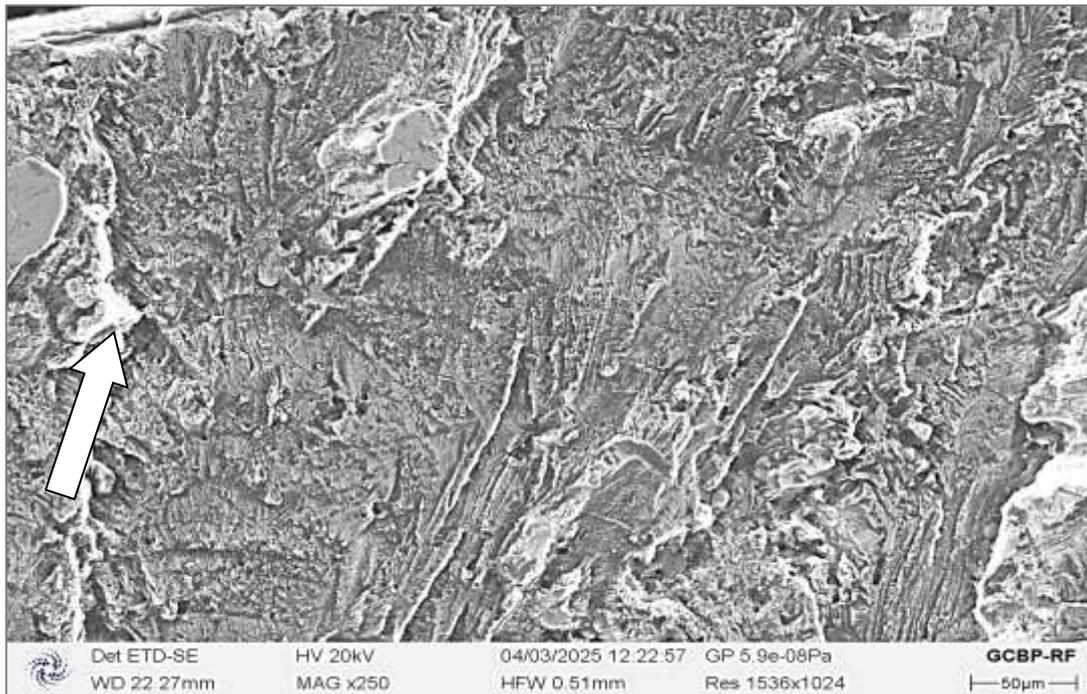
Вид рельефа излома с мезолиниями усталостного разрушения около внутренней поверхности штупера. Стрелка показывает направление роста трещины.
